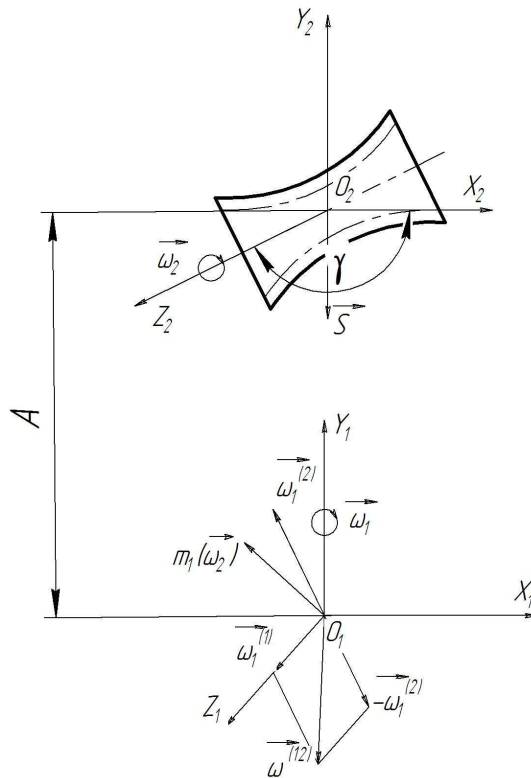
Схема расположения векторов скоростей при притирке зубчатых колес
